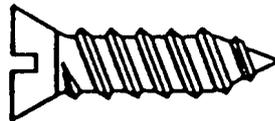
Gewindeformende Schraube (siehe 3.18)
